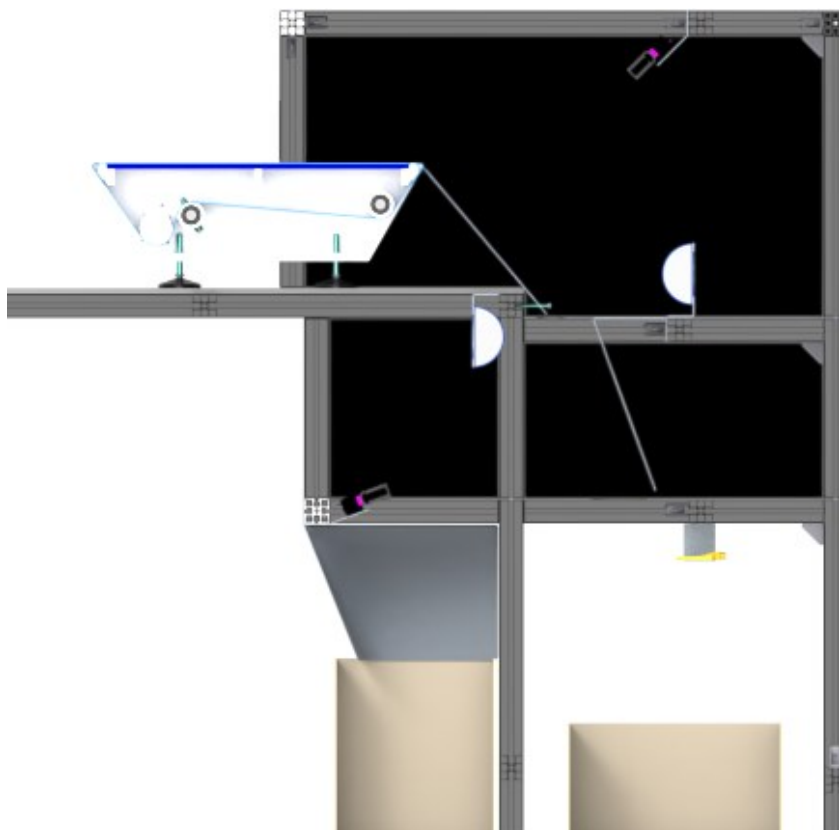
Rendering della sezione laterale della stazione di controllo
